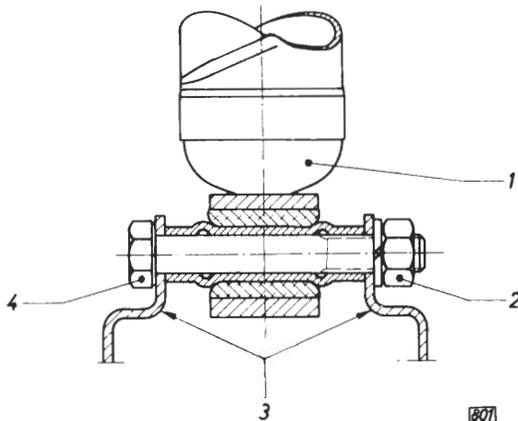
Befestigung Stoßdämpfer am unteren Lenker
